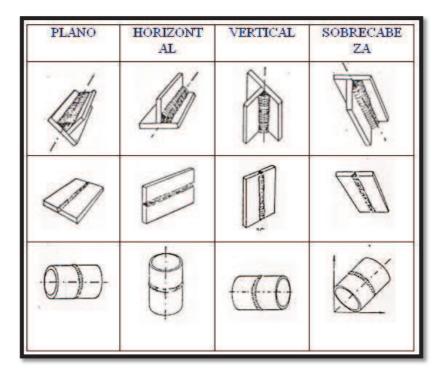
Imagen de las posiciones de soldadura
